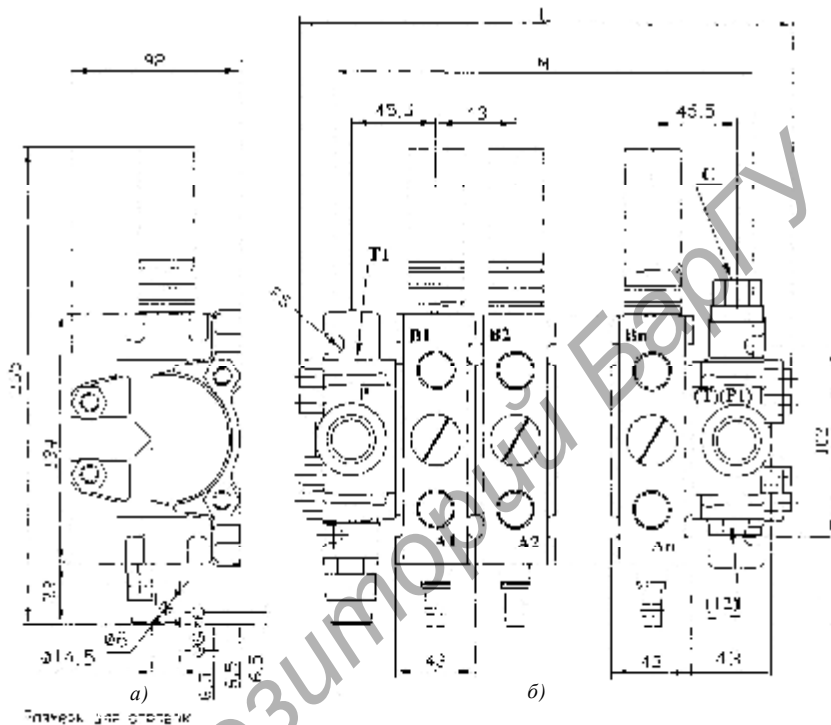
Габаритные и присоединительные размеры распределителя:
